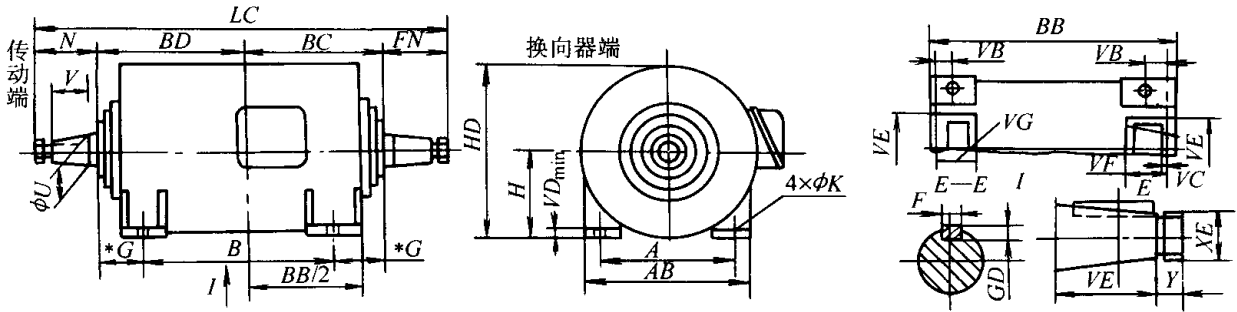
ZZJ800 系列直流电动机外形及安装尺寸图
